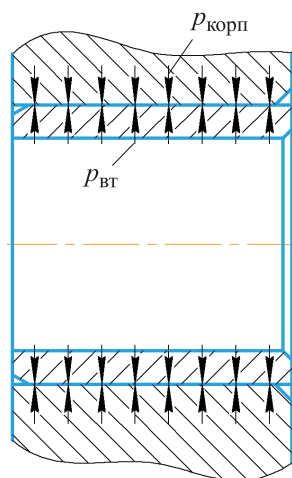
Схема ССН деталей типа «втулка — корпус»: $P_{\text{корп}}$ и $P_{\text{вт}}$ — контактные давления корпуса и втулки
